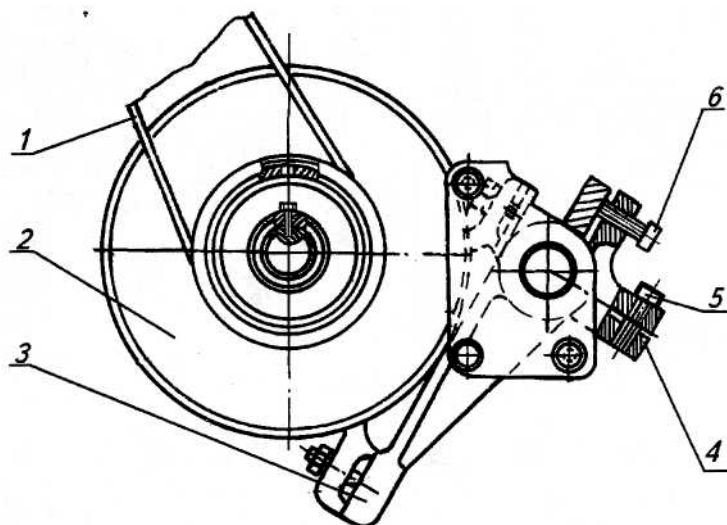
Устройство для натяжения ремней верхнего горизонтального и калевочного суппортов.
